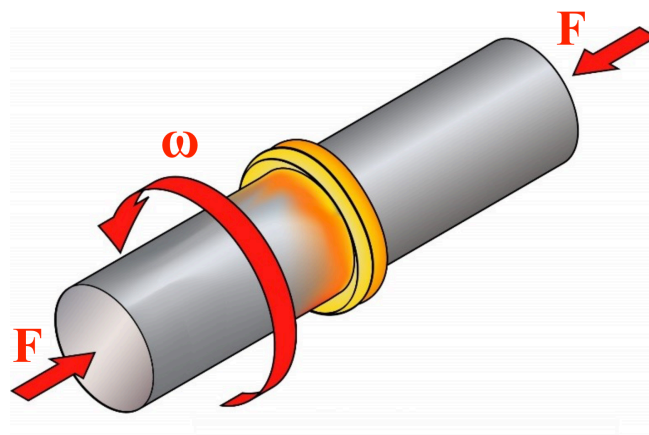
Esquema soldadura por fricción rotacional. [33]
